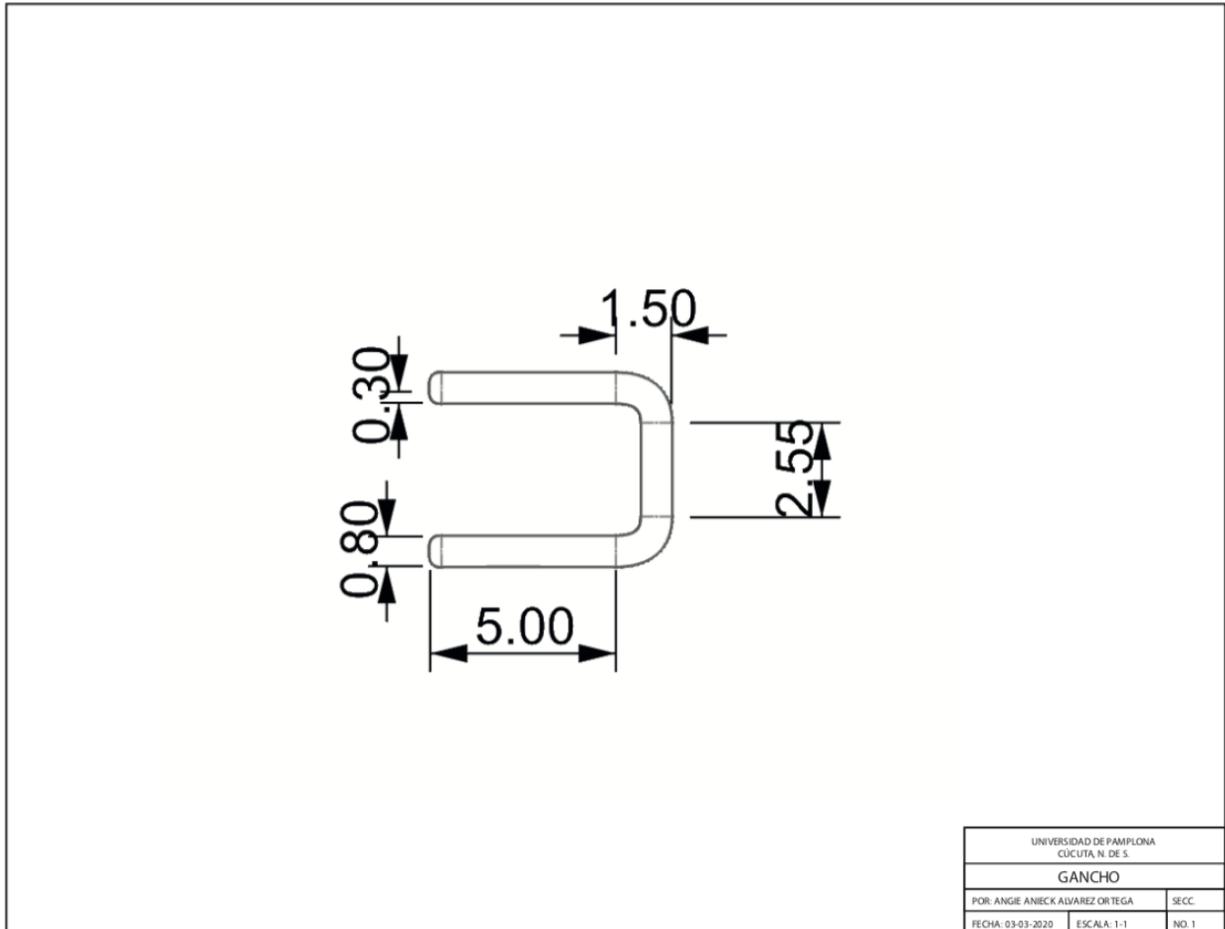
Planos Propuesta Final. Fuente. La Autora.
